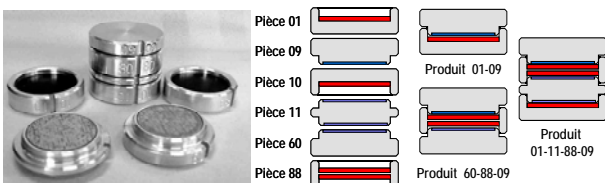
Types de pièces et exemples de produits assemblés sur le SFP
